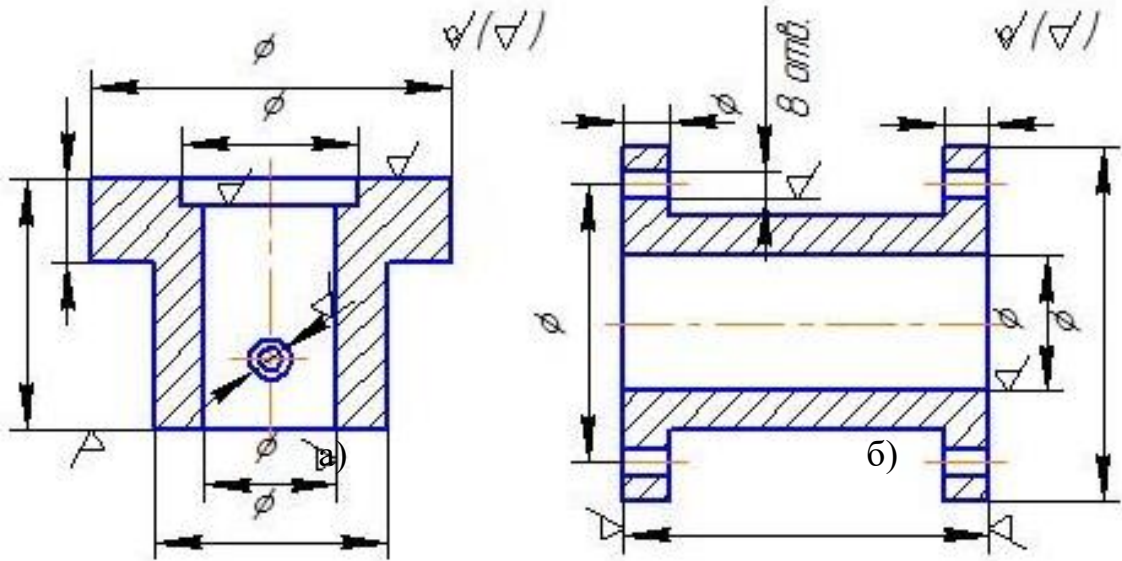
Креслення деталі: а) - сталевий; б) - чавунний
